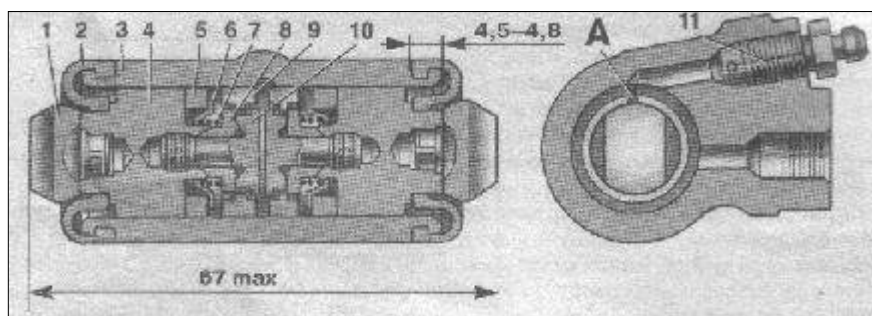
Колісний циліндр: 1 – упор колодки; 2 – захисний ковпачок; 3 – корпус циліндра; 4 – поршень; 5 – ущільнювач; 6 – опорна тарілка; 7 – пружина; 8 – сухарі; 9 – упорне кільце; 10 – упорний гвинт; 11 – штуцер; А – проріз на упорнім кільці.
